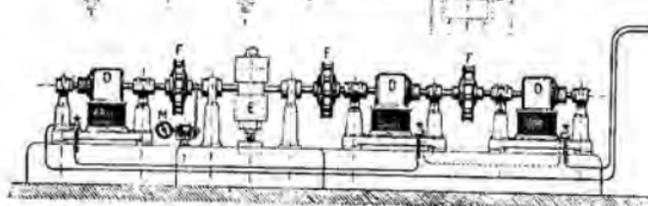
Vue en élévation des trois machines Gramme réceptrices.
